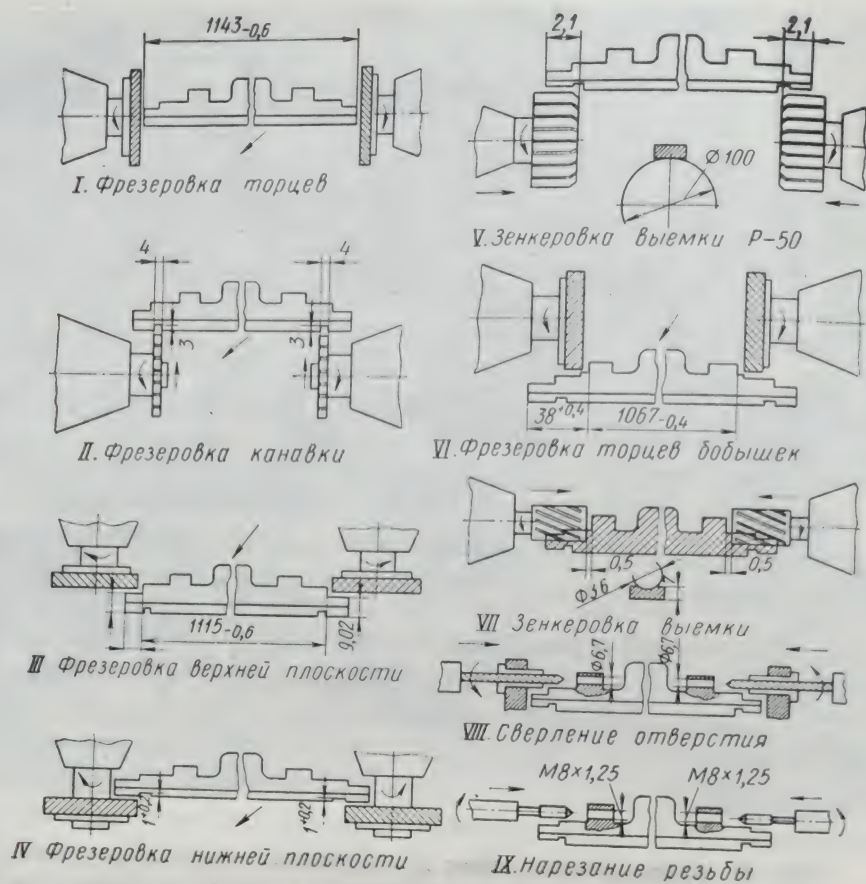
Технологический процесс изготовления детали «шляпка» на автоматической линии
